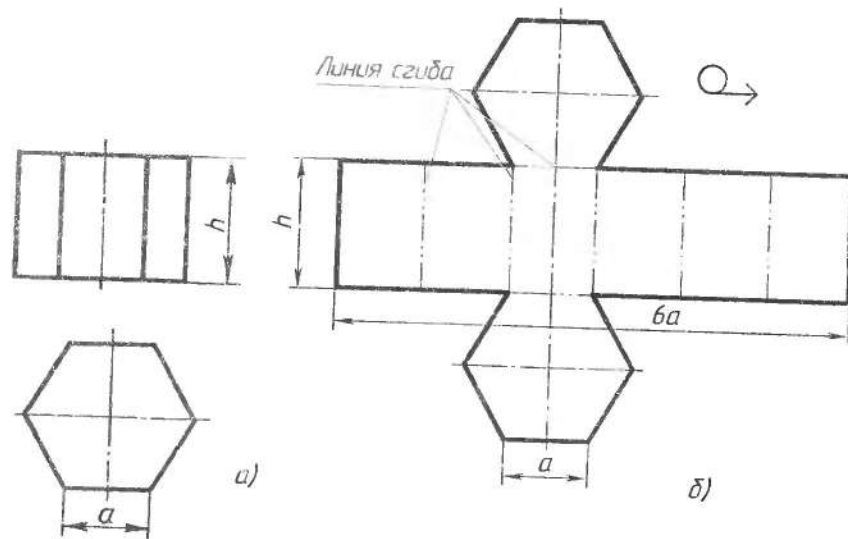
Построение чертежа развертки поверхностей призмы: а — два вида; б — развертка поверхностей
